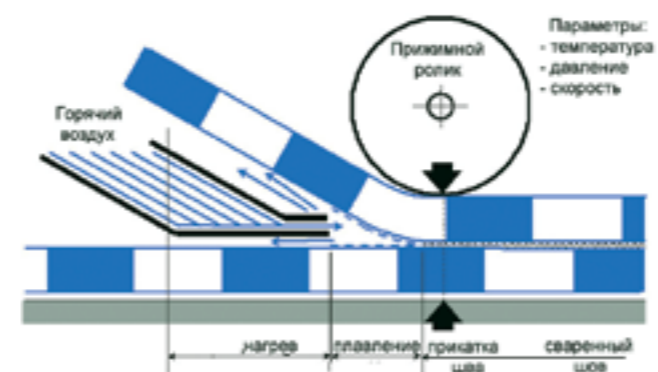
Процесс автоматической сварки.
